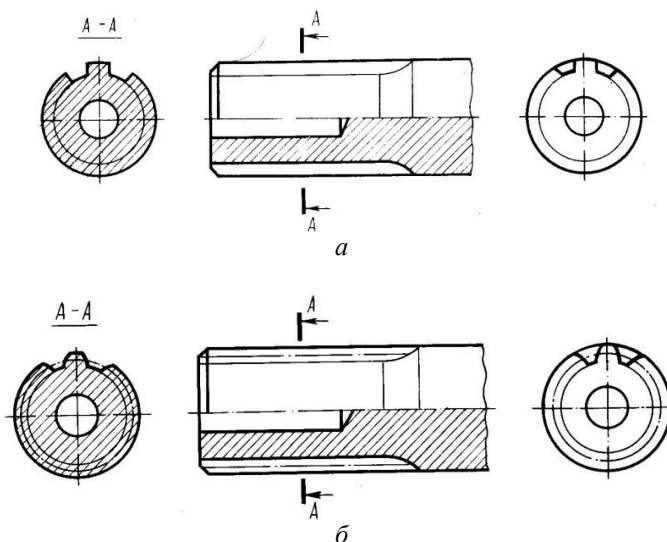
Шлицевой вал: а – прямоугольный, б – эвольвентный
